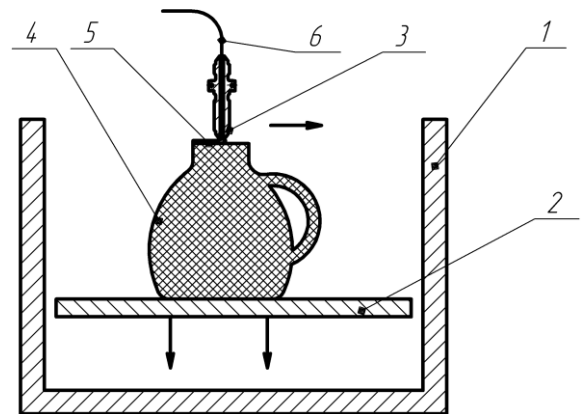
Схема FDM: 1 – корпус; 2 – платформа; 3 – экструзионная головка; 4 – изделие; 5 – отверждаемый слой; 6 – полимерная нить
